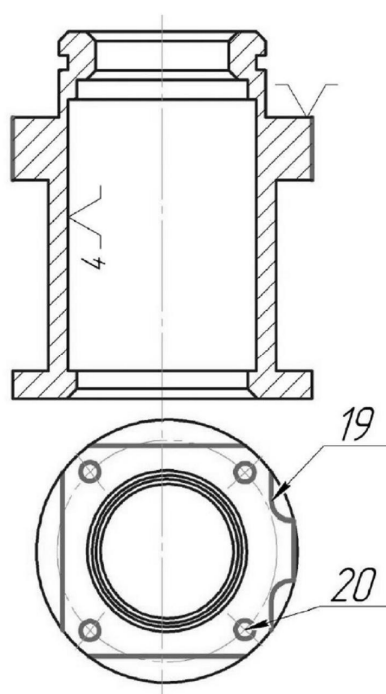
Ескіз для фрезерної операції з ЧПК
